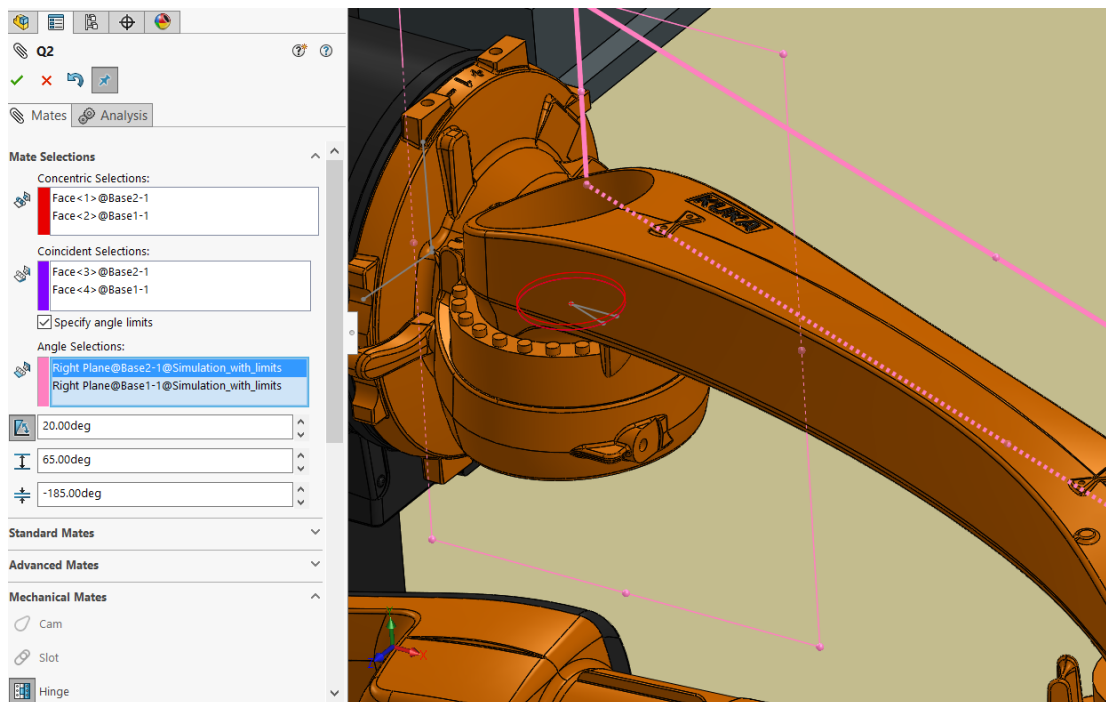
Kuka KR8 R2100HW CAD part
